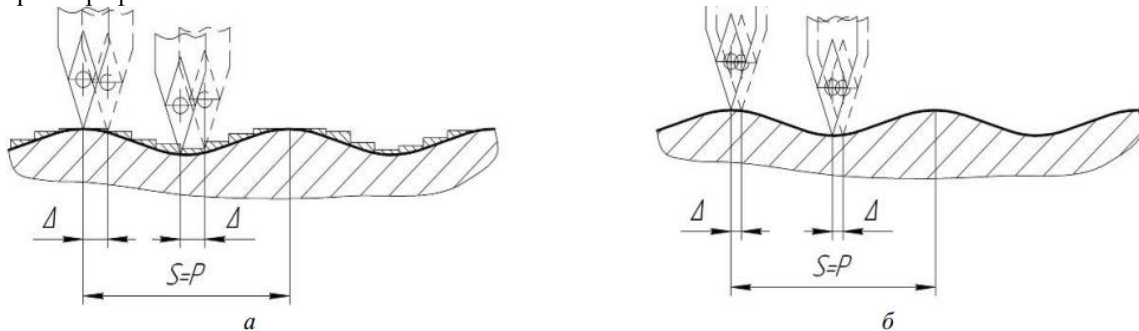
Схема зрізання припуску при точінні внутрішніх різей стандартним різцем: а) чорнова обробка; б) чистова обробка
